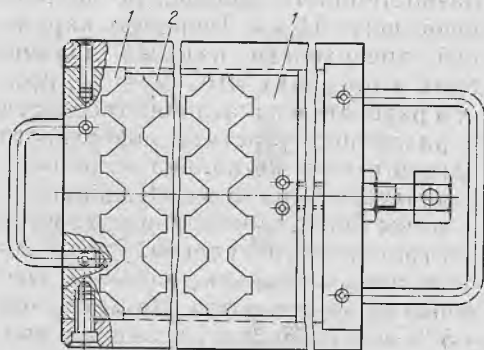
Многоместное приспособление для шлифовки торцов пальцев
